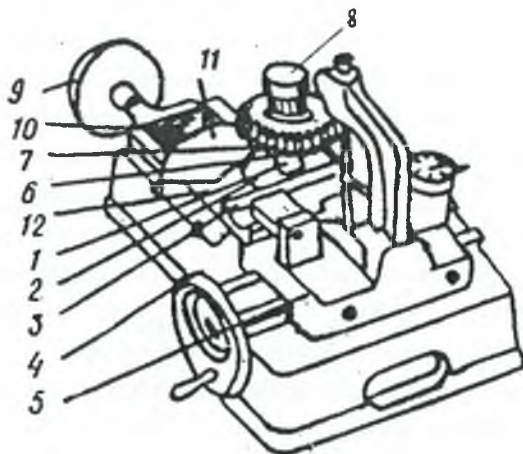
Общий вид эвольвентомера: 1 – оправка эвольвентомера, на которую устанавливается контролируемое колесо; 2 – обкаточный диск с диаметром, равным диаметру основной окружности контролируемого колеса; 3 – линейка; 4 – маховик; 5 – каретка; 6 – цанговый зажим; 7 – измерительный наконечник; 8 – гайка; 9 – маховичок; 10 – пружина; 11 – шкала эвольвентомера; 12 – каретка; 13 – индикатор часового типа; 14 – станина.
